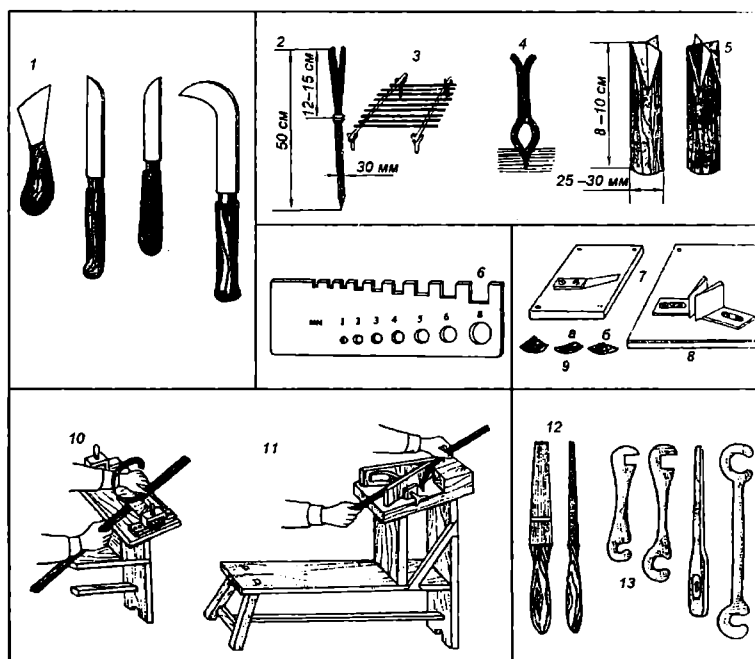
Инструменты для заготовки ивового прута и плетения:
